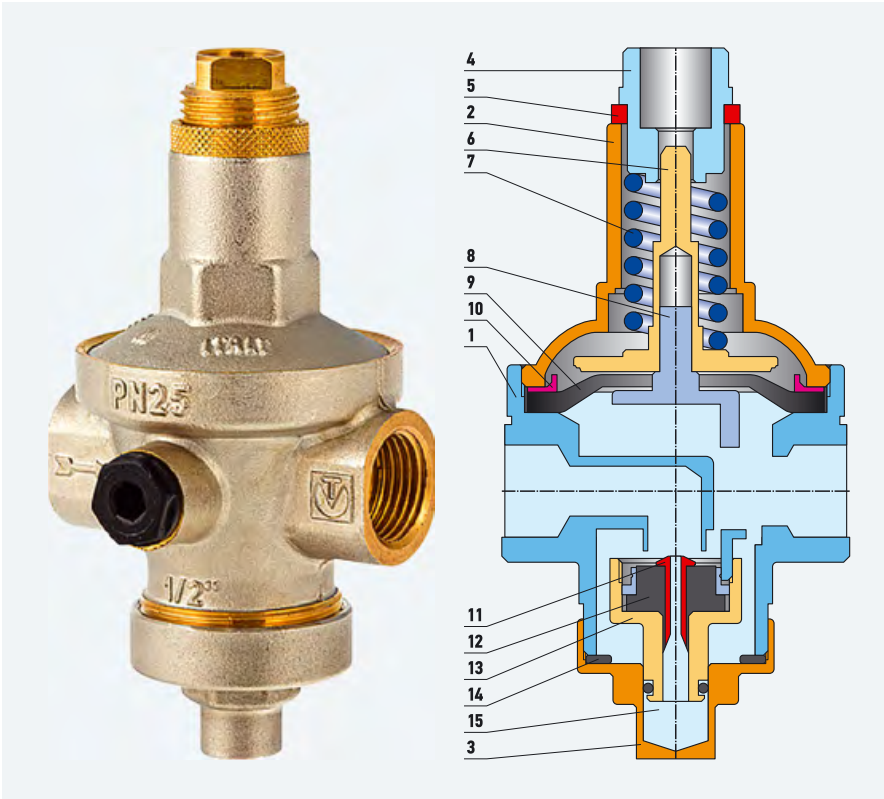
Мембранный редуктор VT.085 (1 — корпус; 2 — крышка корпуса; 3 — пробка корпуса; 4 — настроечная втулка; 5 — фиксирующая гайка; 6 — верхняя часть штока; 7 — пружина; 8 — цилиндрическая часть штока; 9 — мембрана; 10 — распределительное кольцо; 11 — винт золотника с каналом; 12 — золотниковая прокладка; 13 — нижняя часть штока; 14 — уплотнительное кольцо; 15 — демпферная камера)
